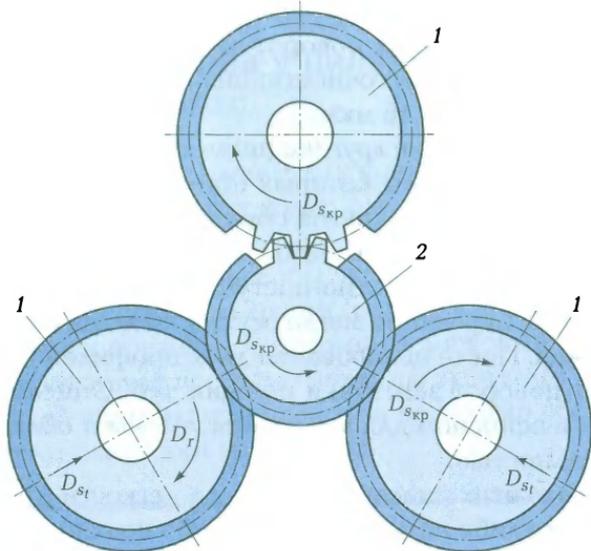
Схема притирки зубчатого колеса тремя притирами-колесами с параллельными осями:
